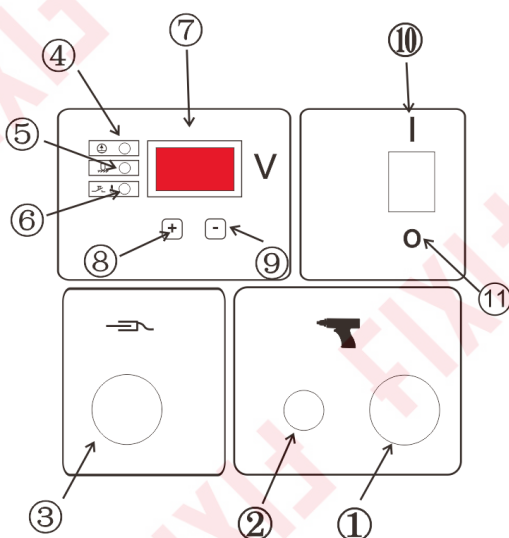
Соединение сварочной горелки и сварочного аппарата
